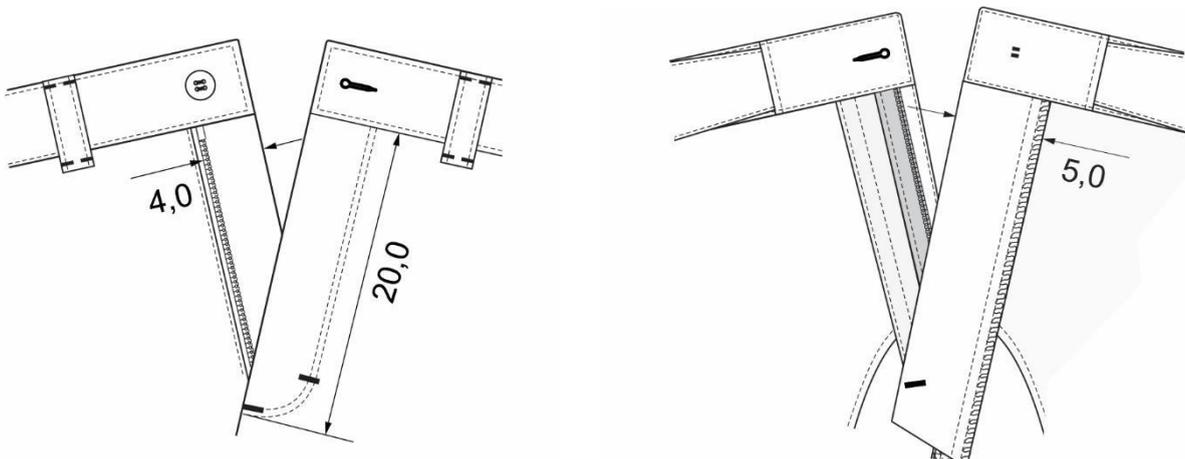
Detalhes da braguilha aberta    Figura 11 – Detalhes internos da braguilha
